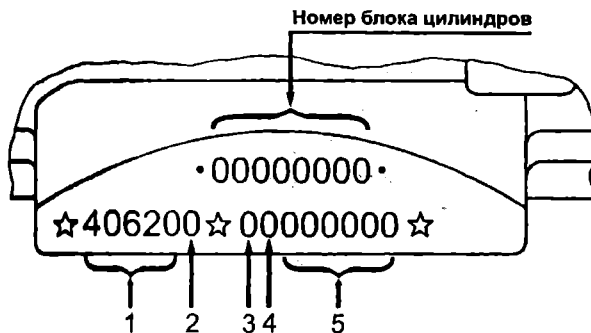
Маркировка на двигателе ЗМЗ-4062
